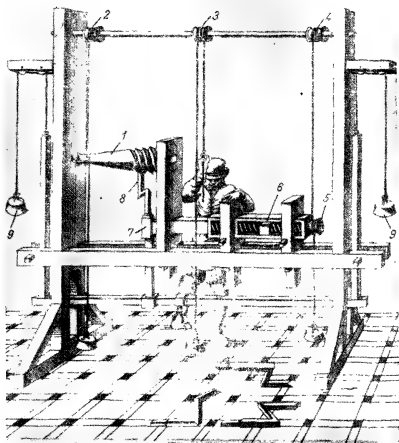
Токарно-винторезный станок. 1569 г. По Бессону.
